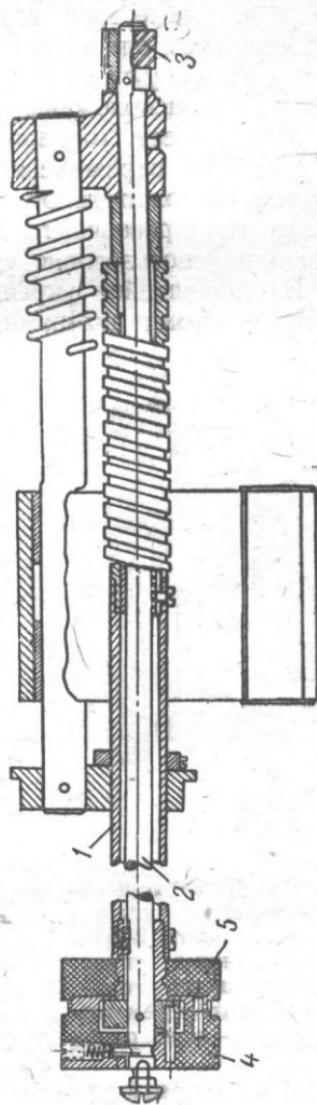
Шпиндельный механизм в разрезе: 1—вал подачи держателя положительного угля; 2—вал подачи держателя отрицательного угла; 3—шестерня; 4—передняя рукоятка; 5—задняя рукоятка
